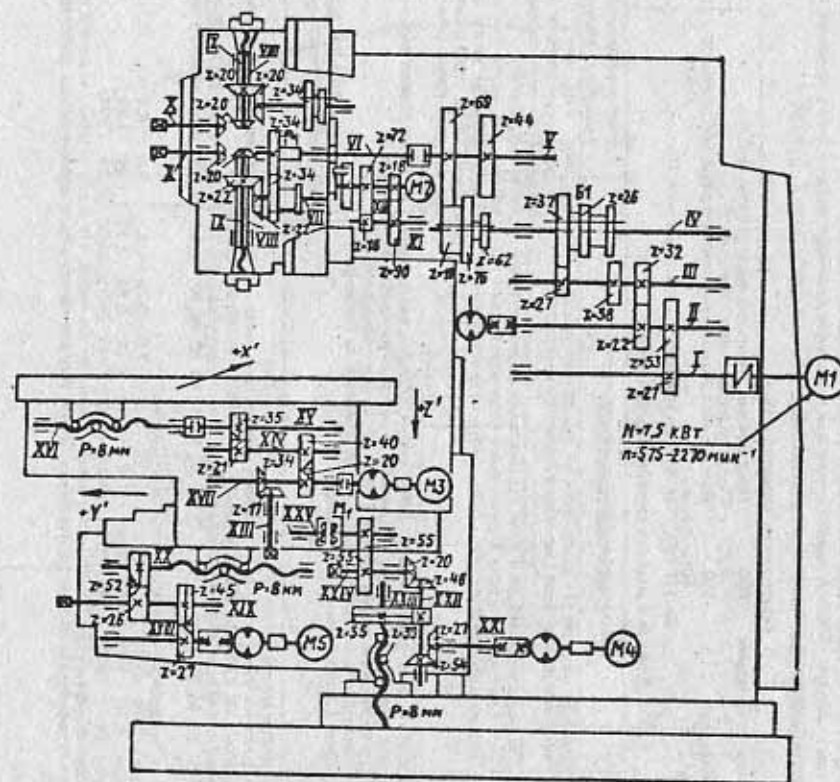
Кинематическая схема вертикально-фрезерного станка мод. 6Р13РФ3 с ЧПУ
